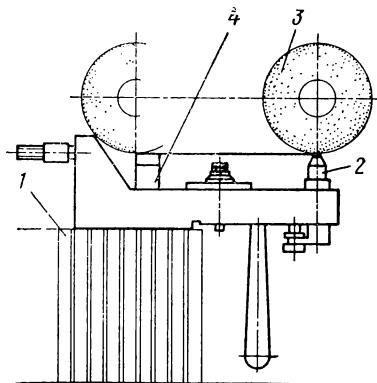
Схема профилирования копирного пальца к приспособлению для круглошлифовального станка:
